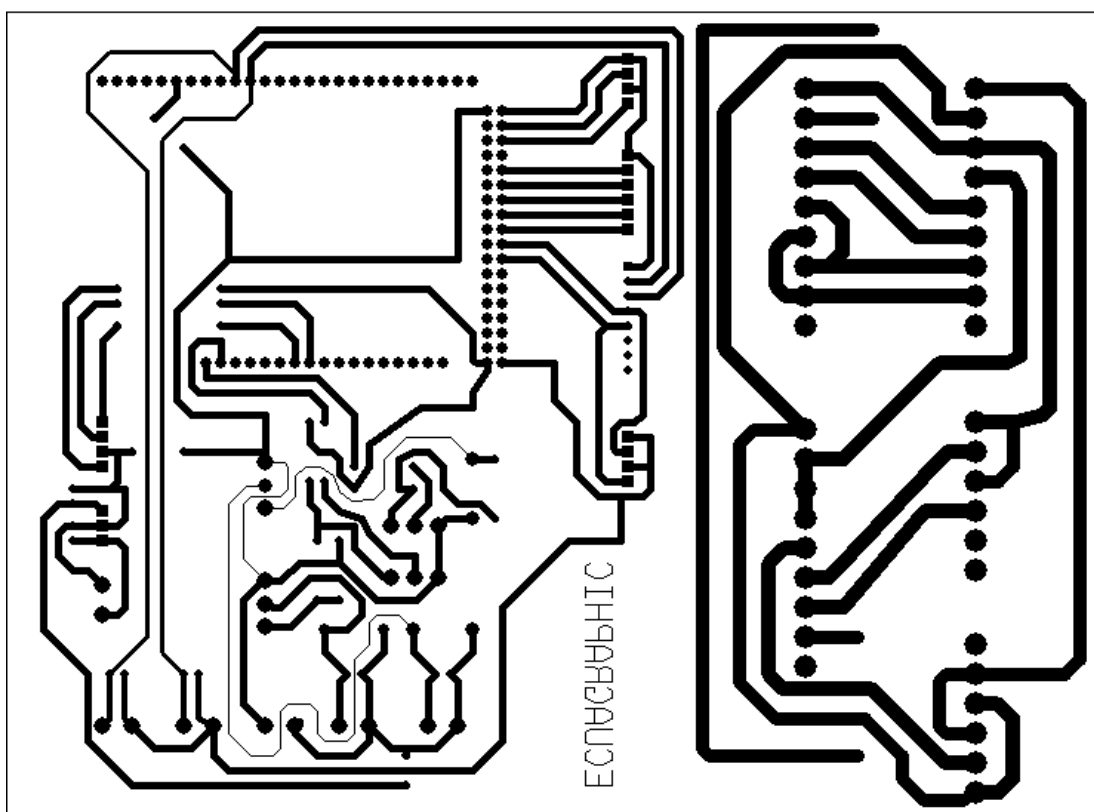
Plantilla de la parte inferior de la placa PCB
